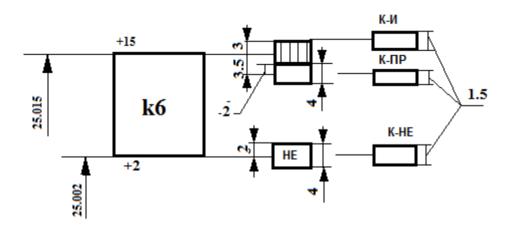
Схема расположения полей допусков калибров для вала Ø25k6 ($^{+0,015}_{+0,002}$)
